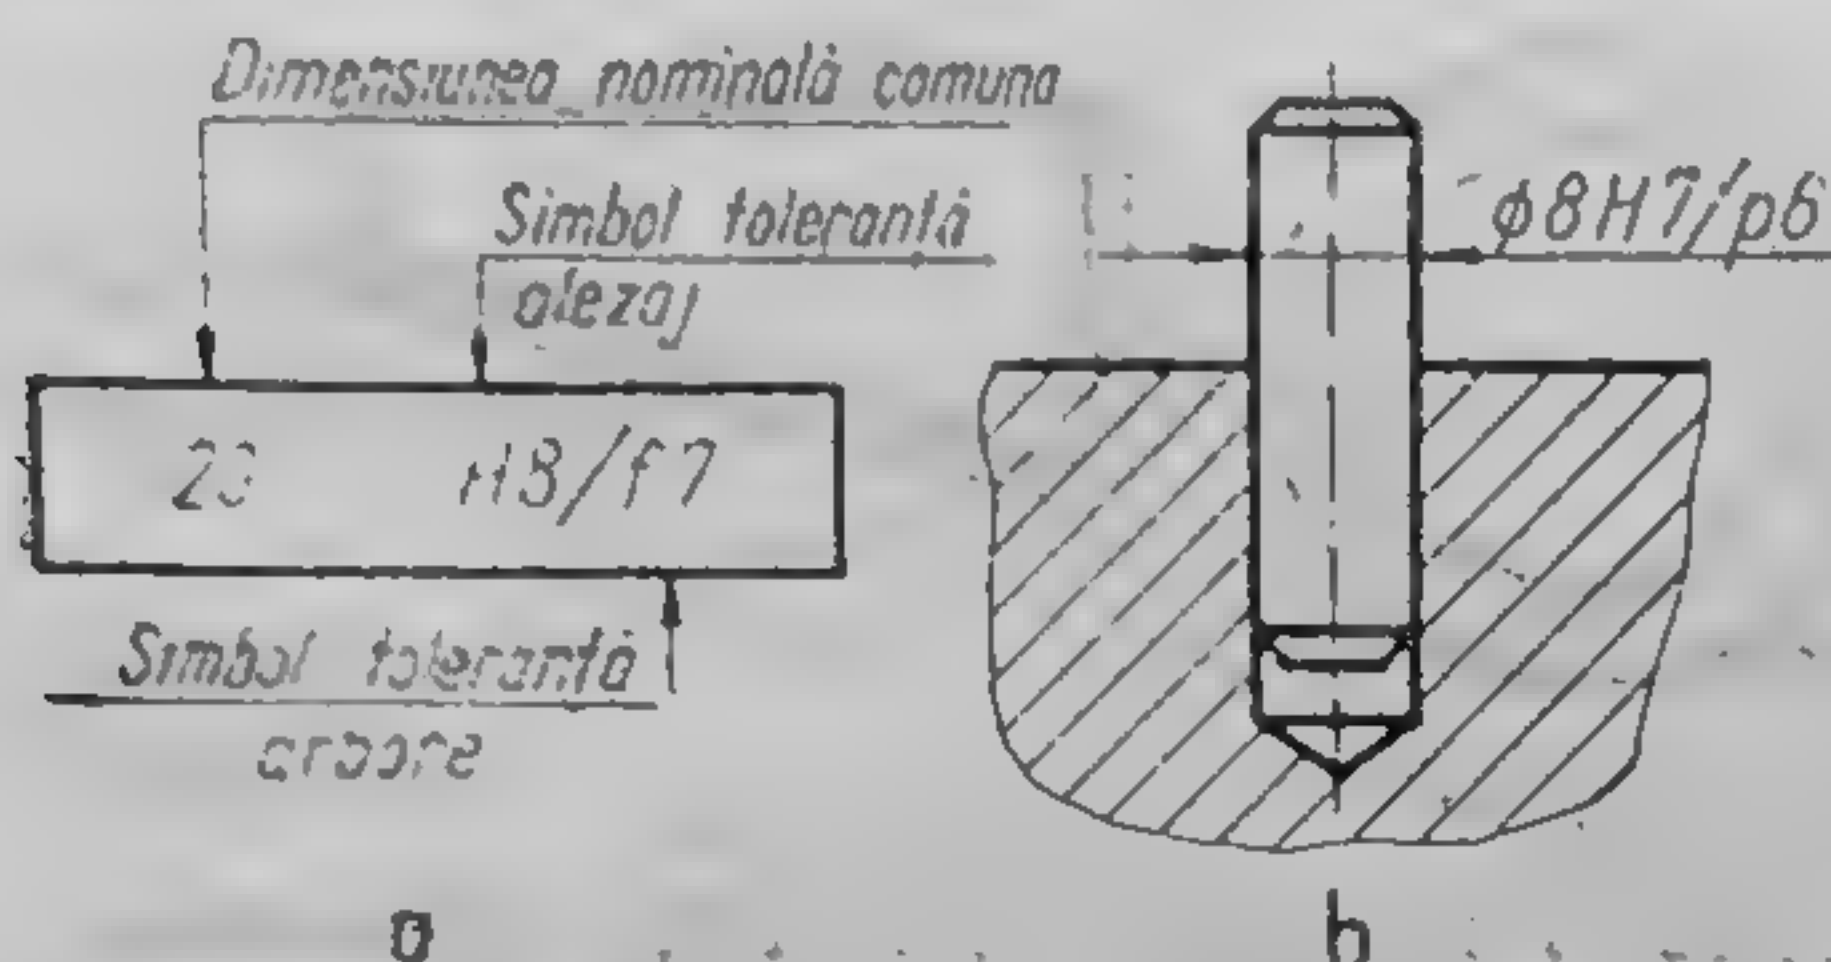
Înserierea toleranței la dimensiunea nominală a ajustajului prin simbolurile celor două câmpuri de toleranță sub formă de fracție, cu linia de fracție oblică :
